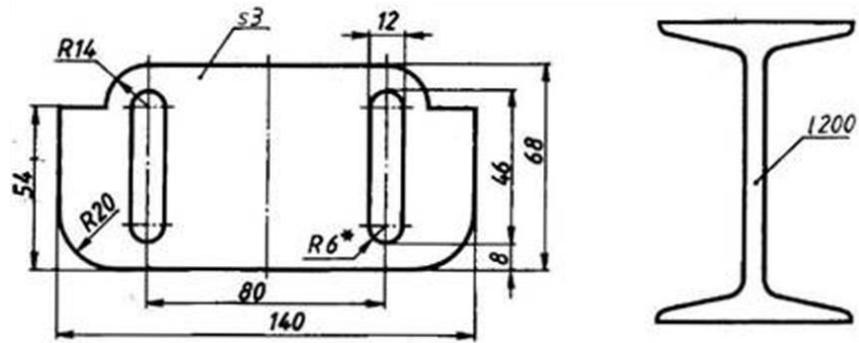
Чертежи плоских деталей с обозначением толщины и длины
